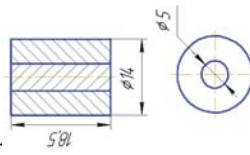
Заготовка под выдавливание компрессорной лопатки
